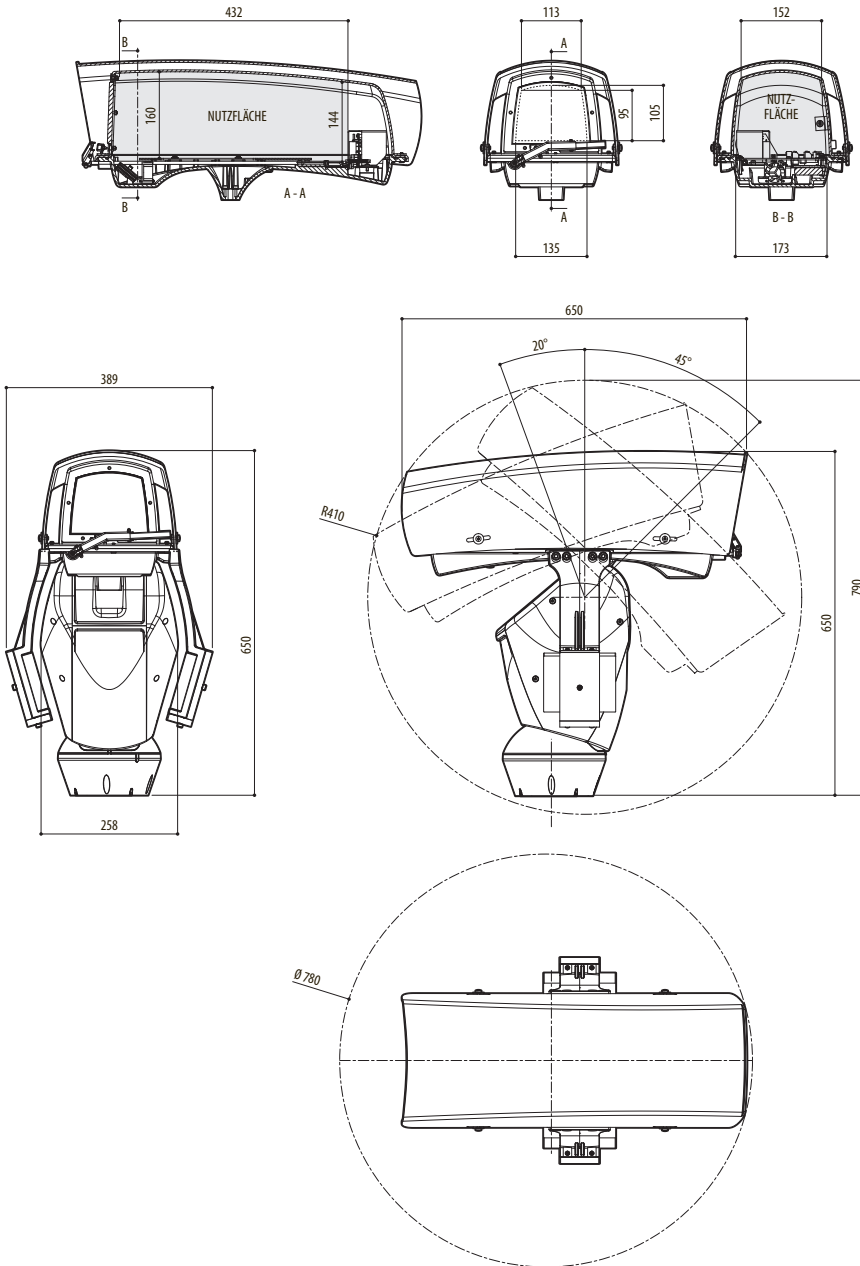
ULISSE MAXI, Standard-Ausführung..
